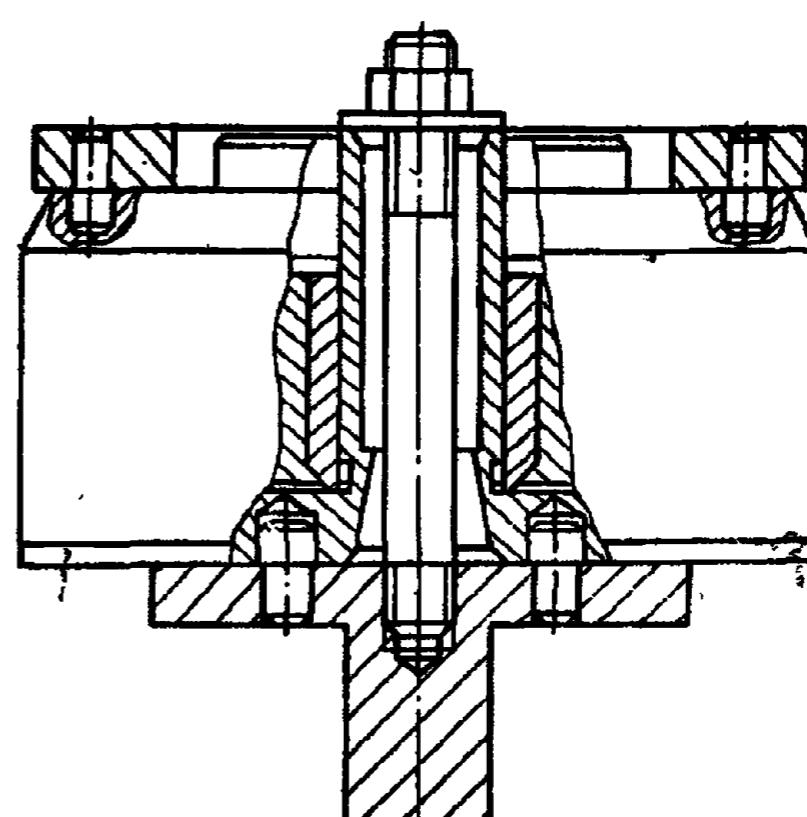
Установка муфты опережения впрыска топлива в приспособление И801.16.000 для разборки-сборки
